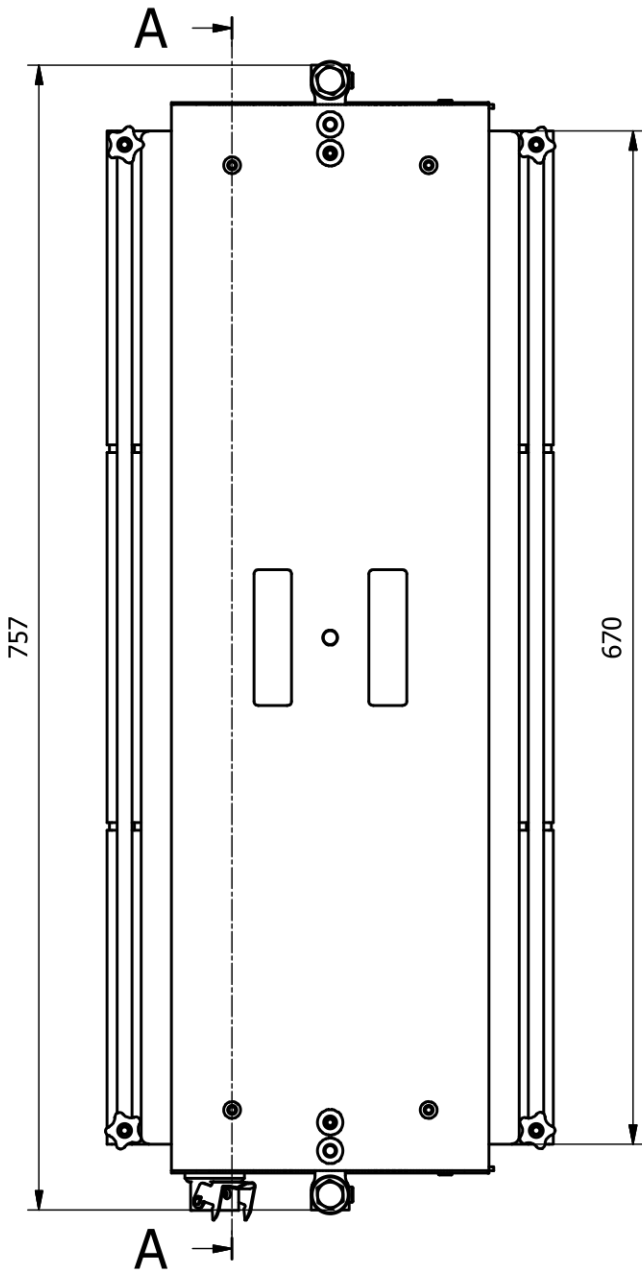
H08D016635 Plaque de soudage PML-300
